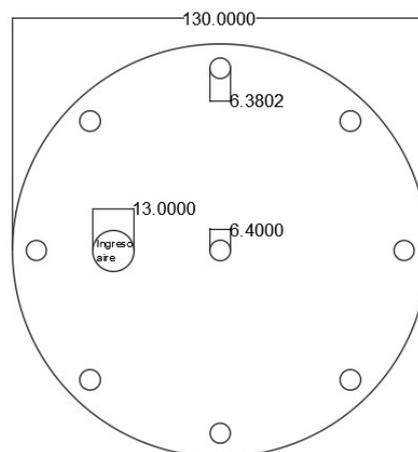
Diseño de la estructura metálica por donde ingresa aire del air caster
